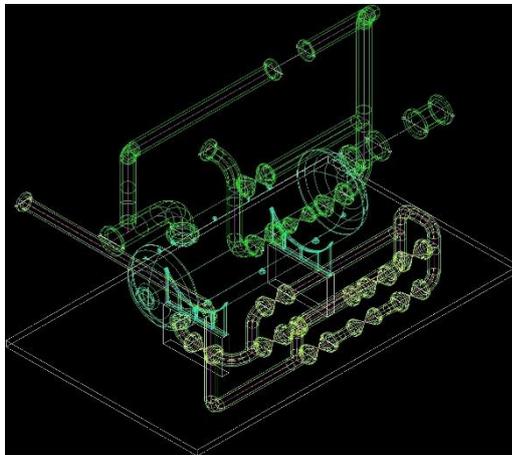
CAD Zeichnung Motor (Designscad, 2021)
